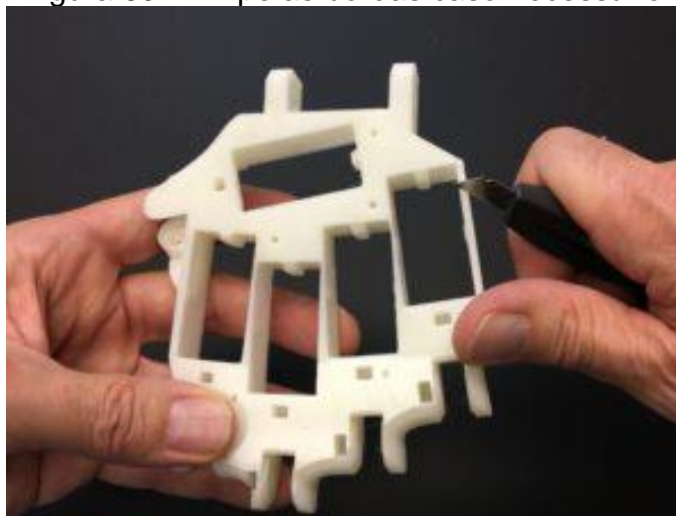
Remover o pedaço de pré-suporte Impresso.
